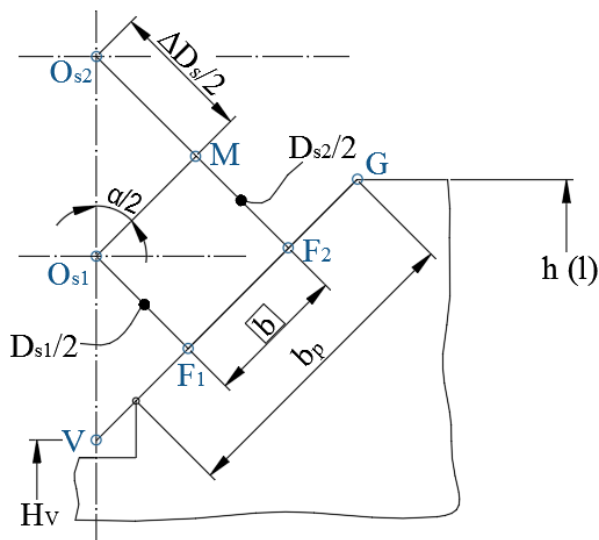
Determinarea geometrică a dimensiunilor unei prisme
